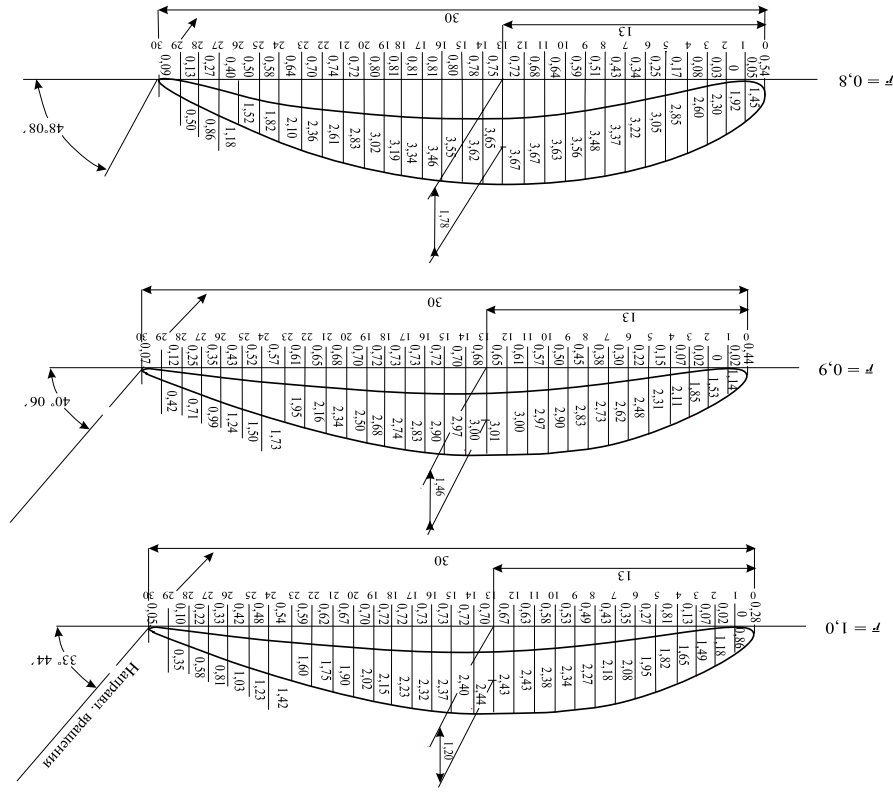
Профили лопатки рабочего колеса ступени К-70-17
